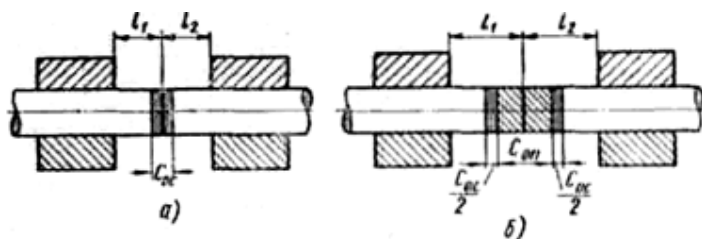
Схема установки свариваемых деталей при стыковой сварке:
